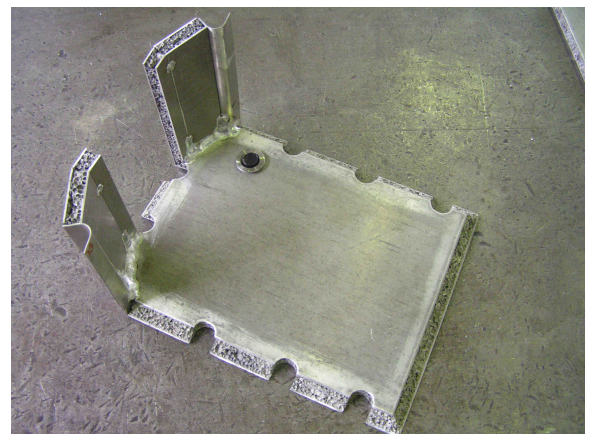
Schräge Wandelemente mit Bodenplatte verschweißt
